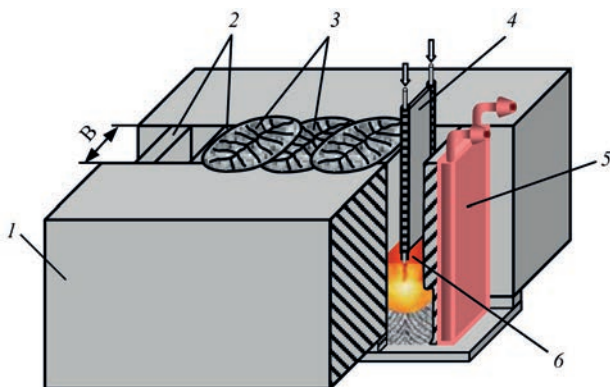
Схема способу БЕШЗ ПМ масивних виробів з великим перетином з'єднувальних елементів: 1 – зварювана деталь; 2 – формуючі перегородки; 3 – зварні шви; 4 – плавкий мундштук; 5 – охолоджуваний водою формуючий пристрій; 6 – шлакова ванна; В – зварювальний проміжок
